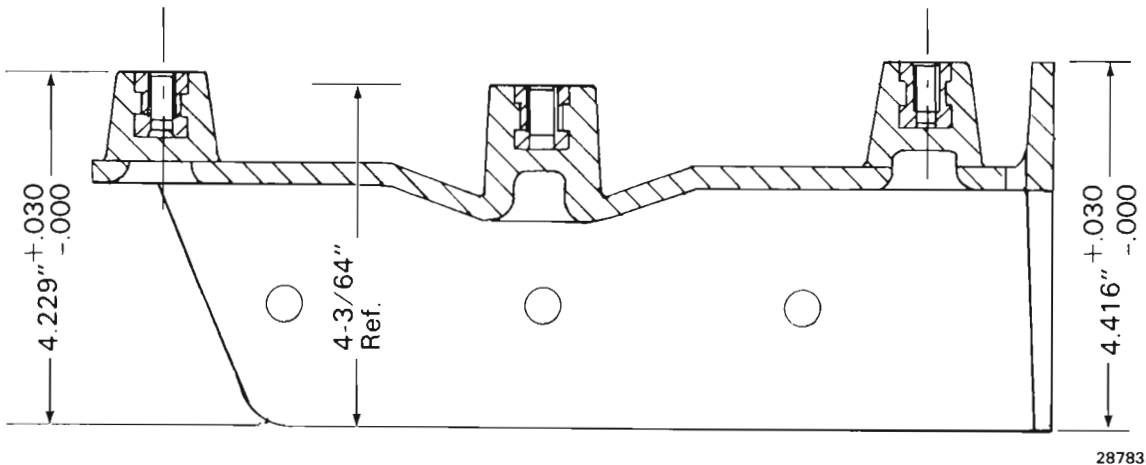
Corte transversal de la hoja lateral con aisladores moldeados
